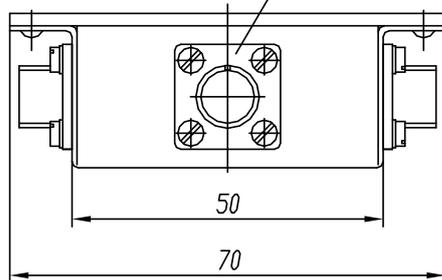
Габаритный чертеж коробки КСР2-1К-А
